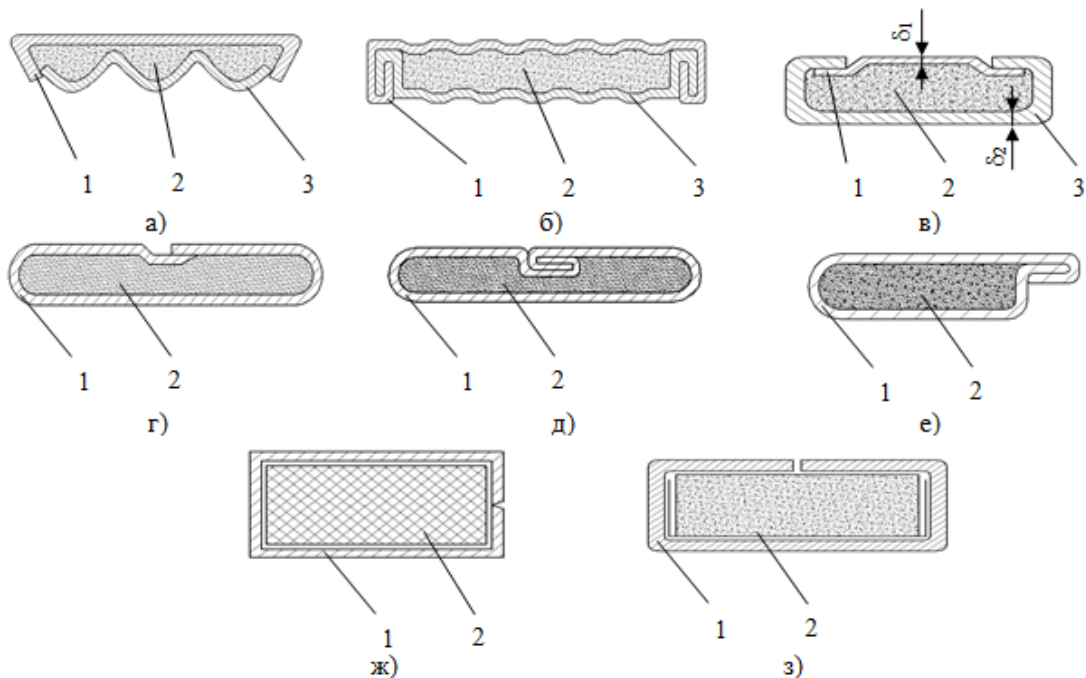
Общий вид сечений порошковых лент различных конструкций:
